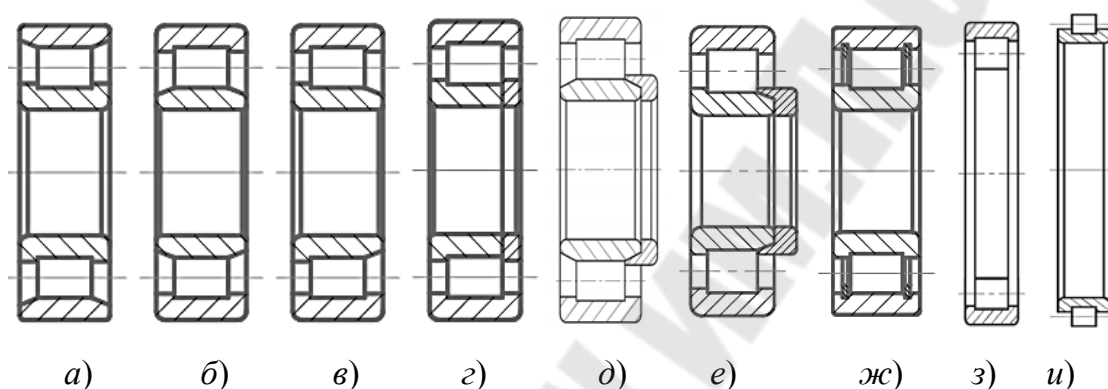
Конструктивные разновидности роликоподшипников с короткими цилиндрическими роликами
